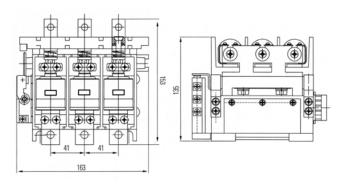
Габаритные размеры КВТ-1,14-80/125/160
